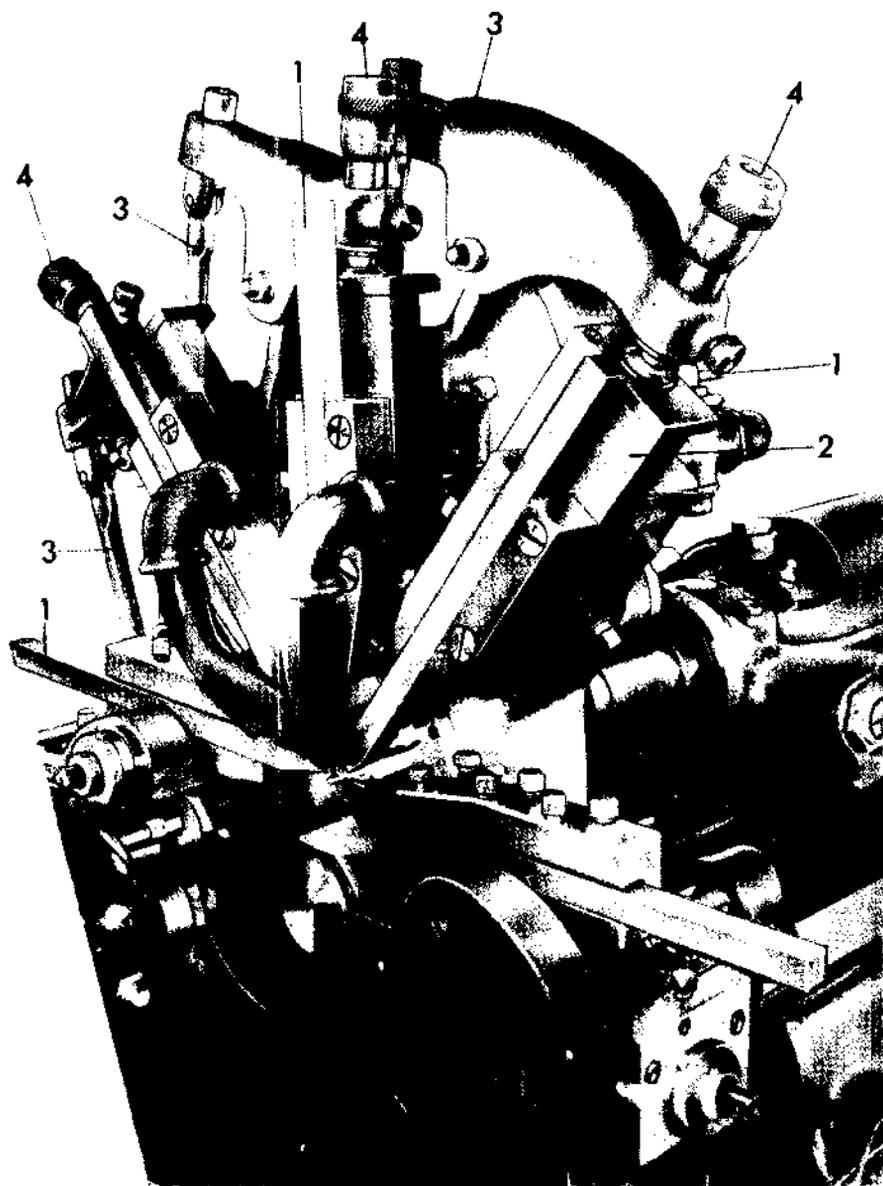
Detalle de los portaherramientas del torno de la figura 739. 1, herramientas; 2, carros portaherramientas, 3, palancas de mando; 4, pomos de regulación
